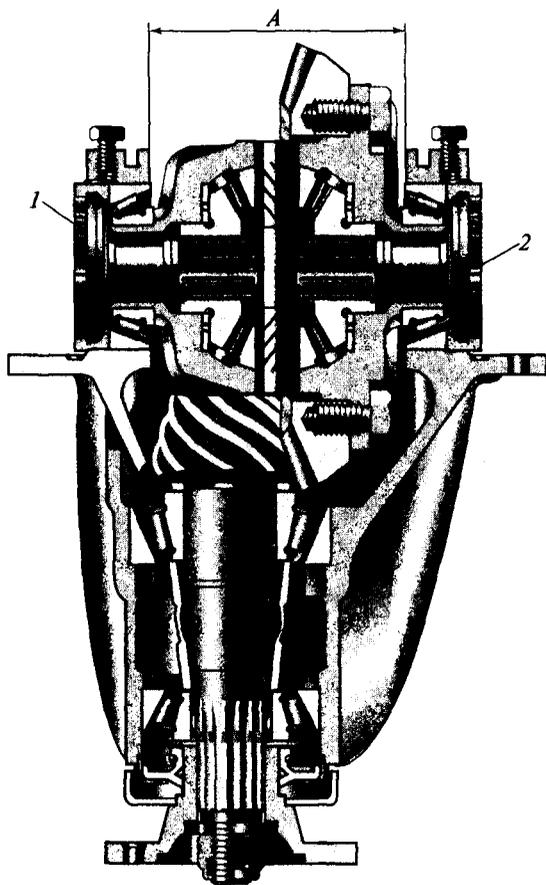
Схема проверки предварительного натяга подшипников коробки дифференциала:
